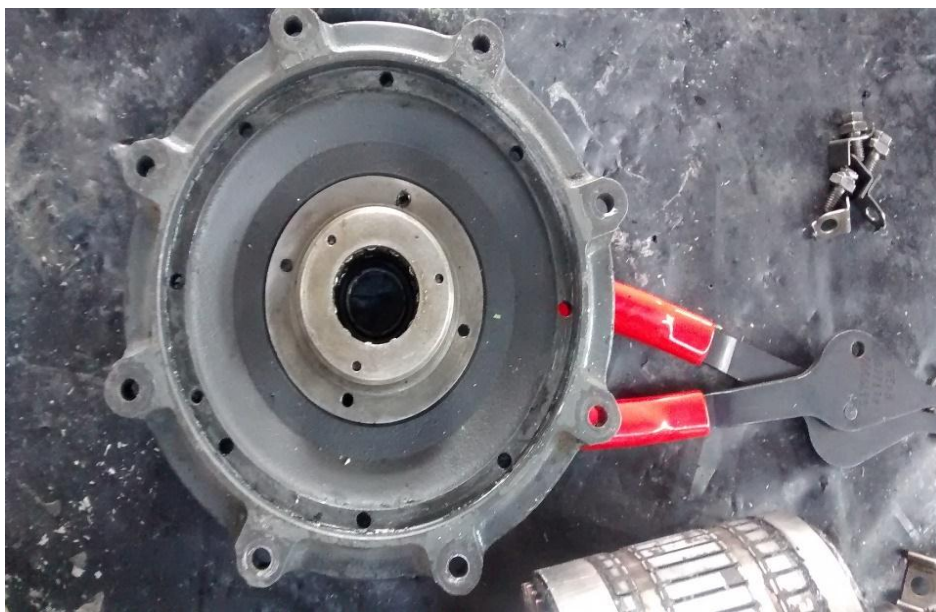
Limpieza rotor, banda y tapa de la carcasa del starter
